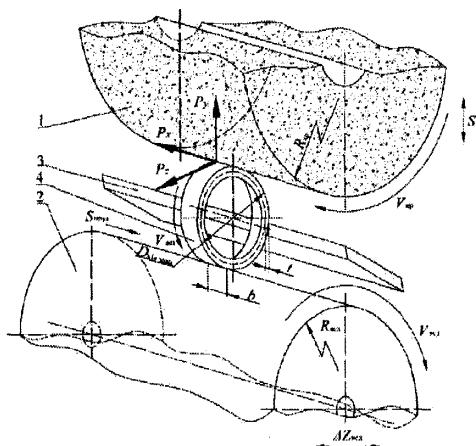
Розрахункова схема процесу шліфування: 1 – шліфувальний круг; 2 – ведучий круг; 3 – ніж опорний; 4 – заготовка
